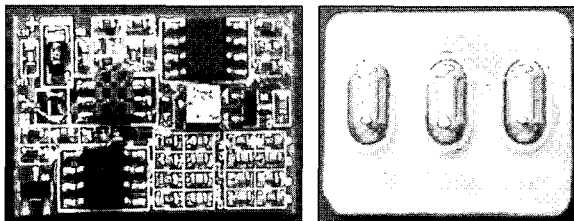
개발된 근전위 센서의 PCB 및 전극부
